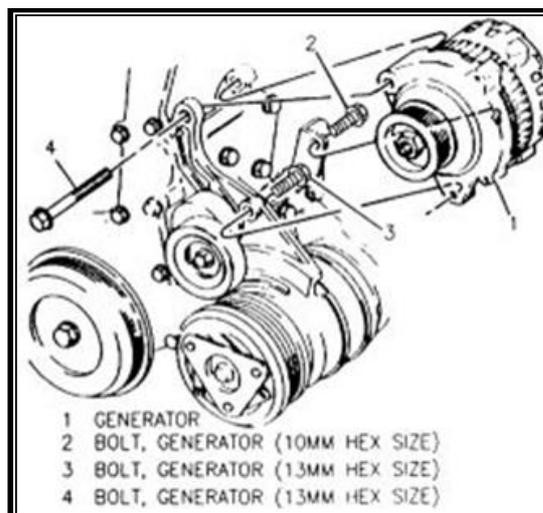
Par de apriete del alternador. (AutoZone, 2018)
